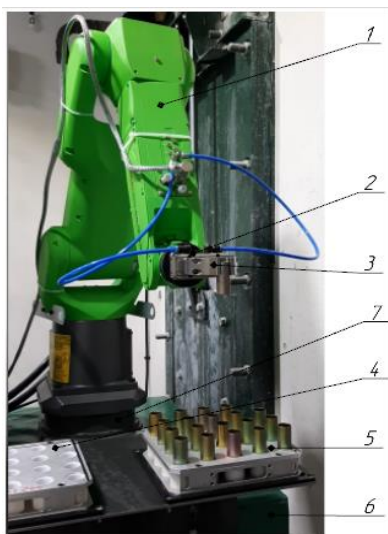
Общий вид механизма досылки-разъема пресс-инструмента:
